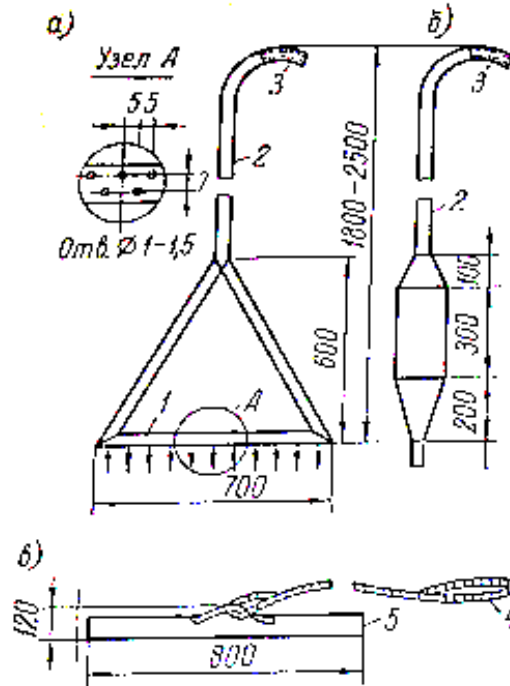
Схема устройства для паротепловой резки льда:
